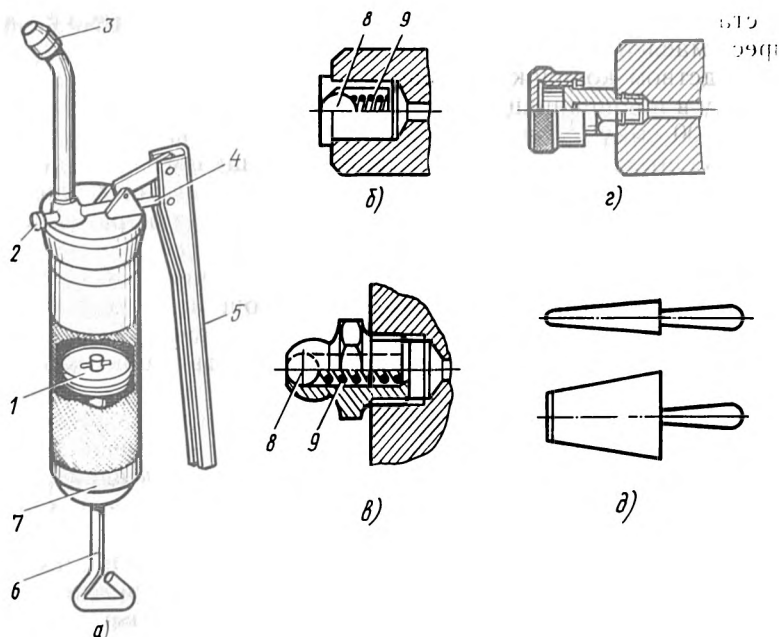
Устройства для смазывания деталей крановых механизмов: а — рычажный шприц, б — ниппельная пресс-масленка, в — шариковая пресс-масленка, г — колпачковая масленка, д — лопатка (шпатель); 1 — поршень, 2 — обратный клапан, 3 — наконечник, 4 — плунжер, 5 — рычаг, 6 — шток, 7 — корпус, 8 — шарик, 9 — пружина
